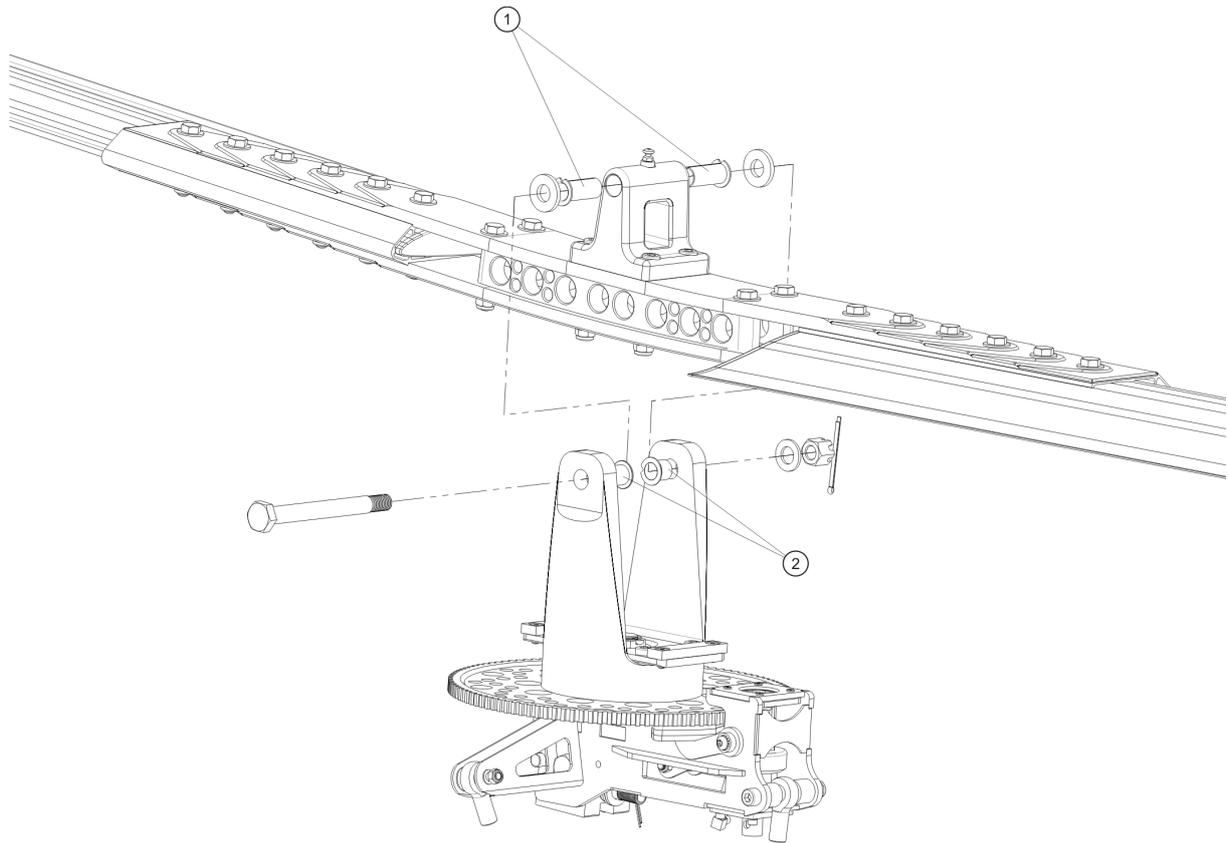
Teeterlager Buchsen, Block und Turm - Explosionsansicht
